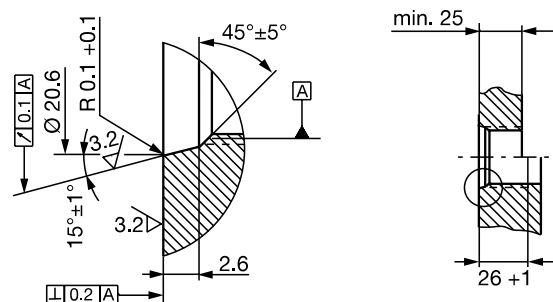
Einschraubloch 3/4"-16UNF nach SAE J475 O-Ring 15.3x2.4
